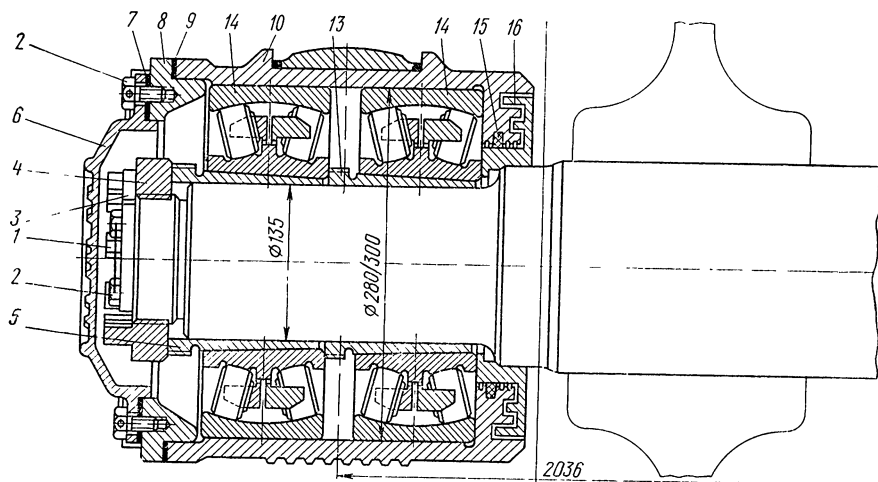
Букса с двумя роликовыми сферическими подшипниками (позиции — см. подпись к рис. 7)
